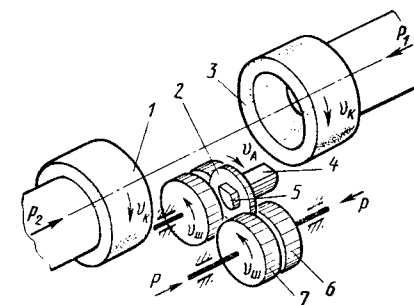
Схема двустороннего торцового шлифования фрез
